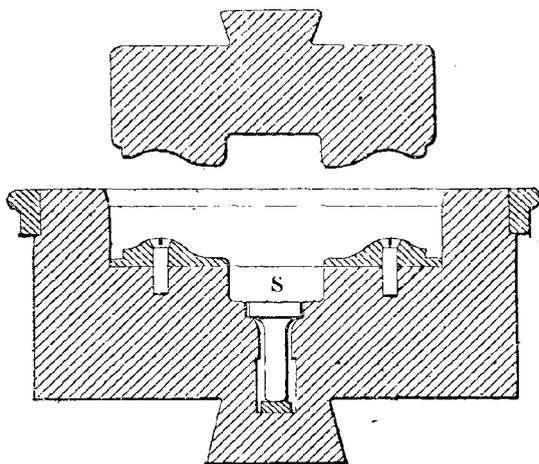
Dernier forgeage des roues pleines en fer forgé.
